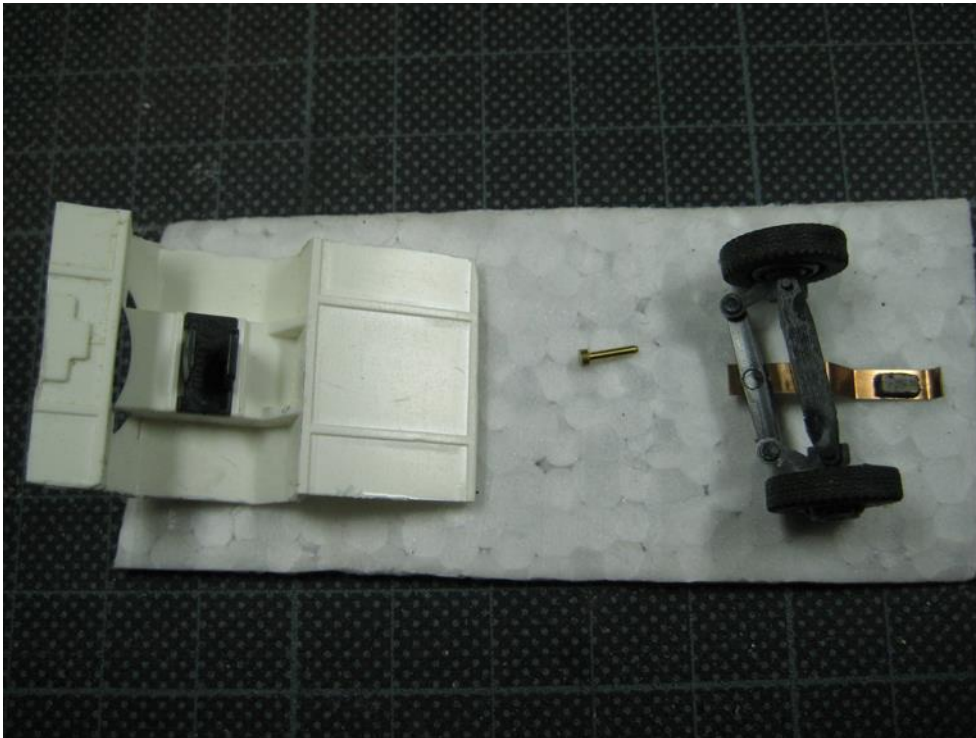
stuuras verwijderd door de scharnierpen er uit te halen.
